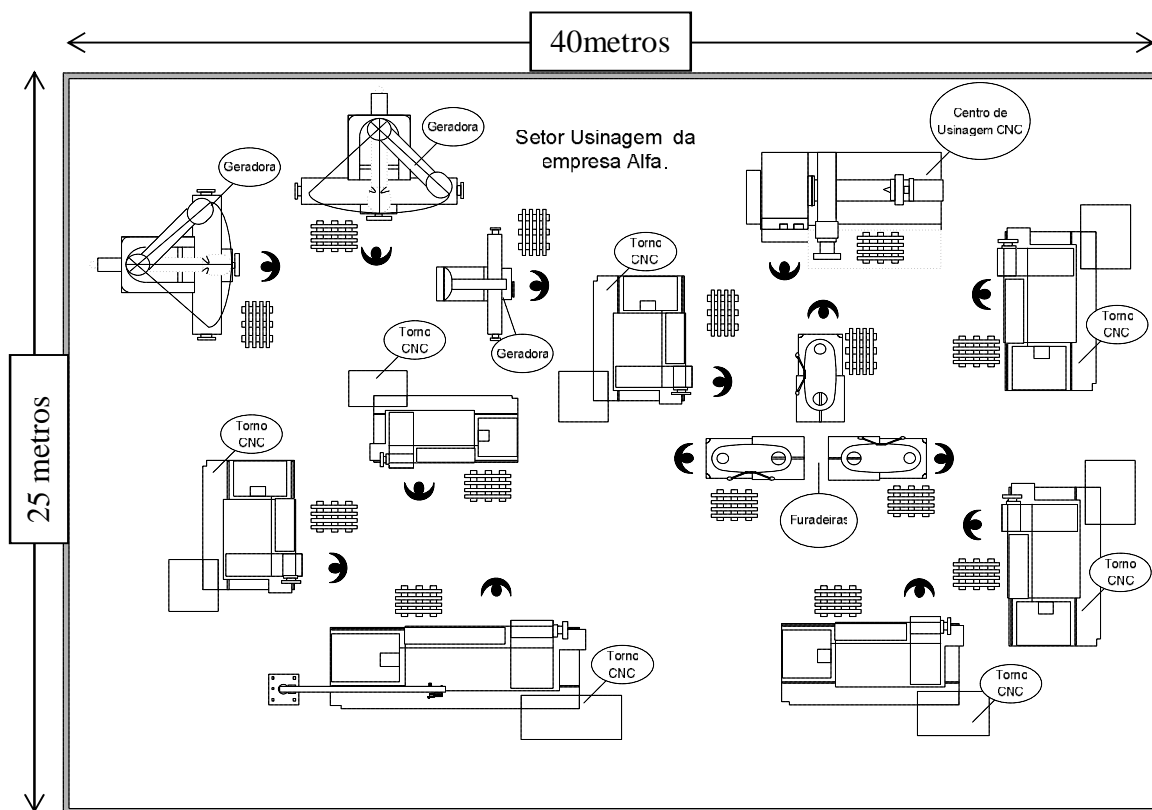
Arranjo físico (*layout*) do setor usinagem.
